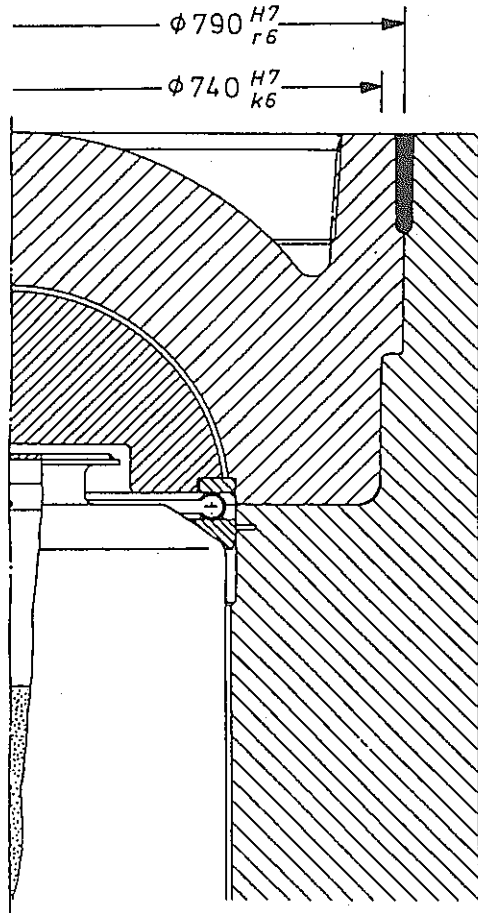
Eingeschrumpfter Behälterdeckel
